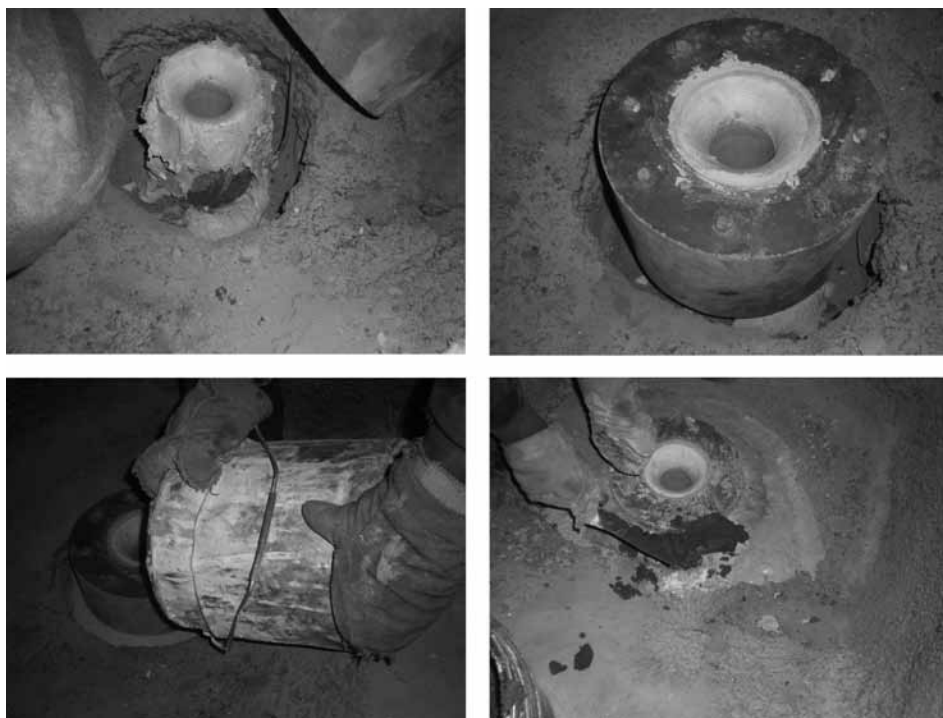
Внешний вид и установка кольцевого продувочного блока в дне промежуточного ковша слябовой МНЛЗ ПАО «Алчевский металлургический комбинат»
